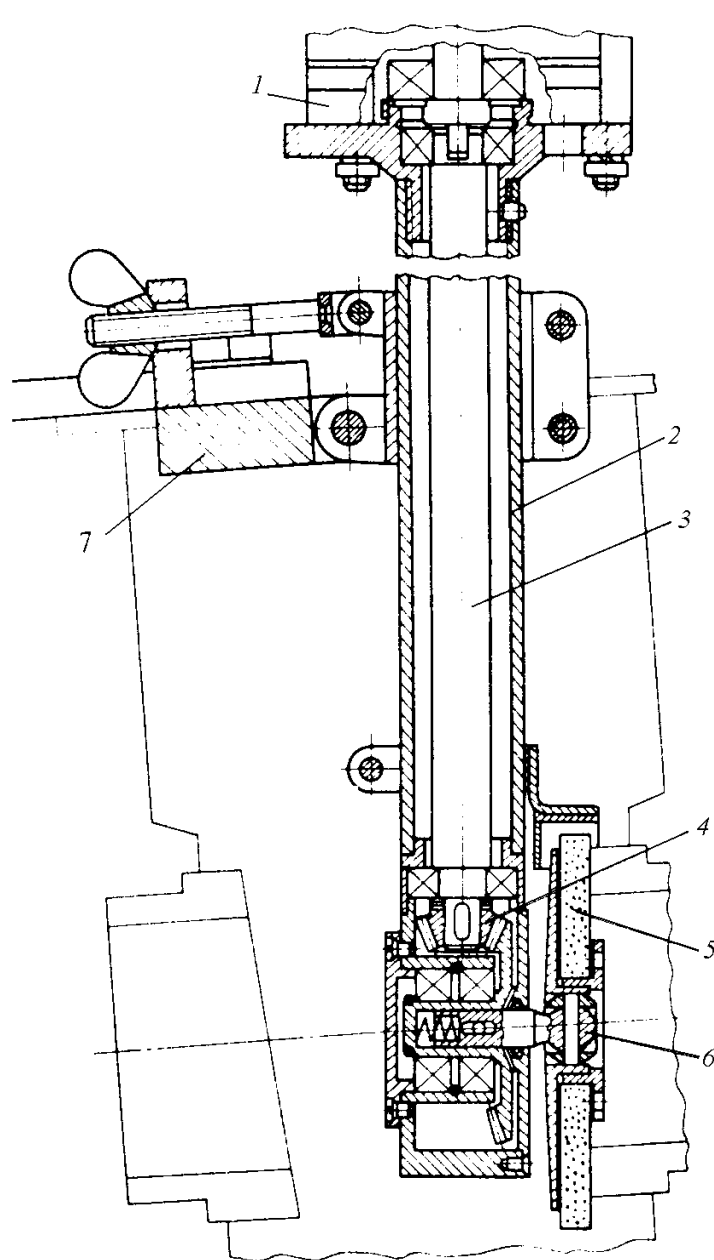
Приспособление для шлифовки седел бесфланцевых задвижек.
